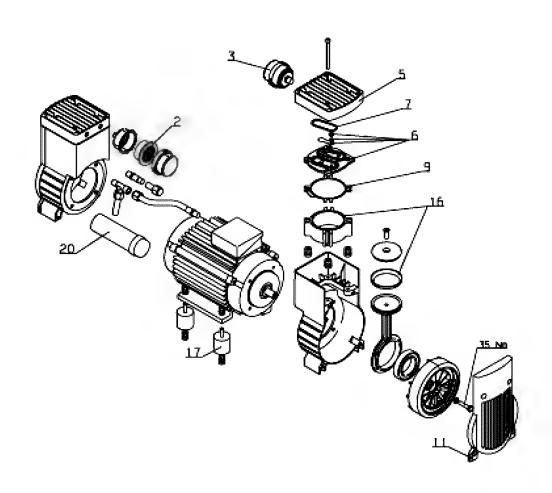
Чертеж составных частей компрессора D-100
